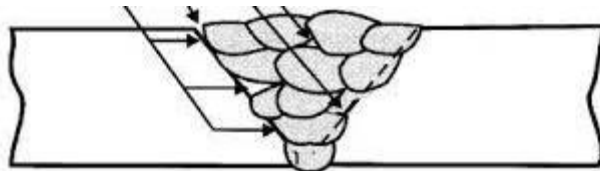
Indicaciones de falta de fusión entre pases de soldadura y cara de soldadura.
